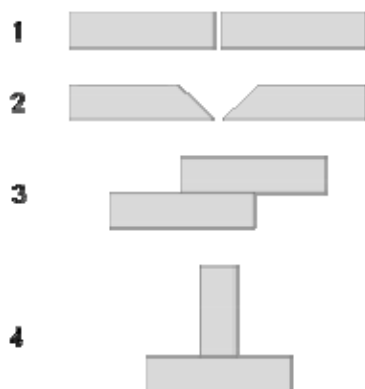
Tipos comunes de juntas de soldadura
